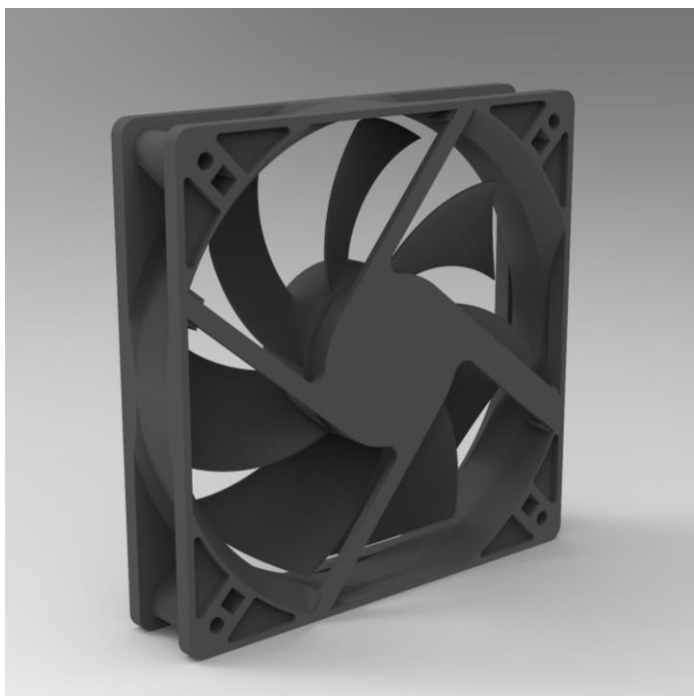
Detail umístění odvlhčovacího mechanismu
